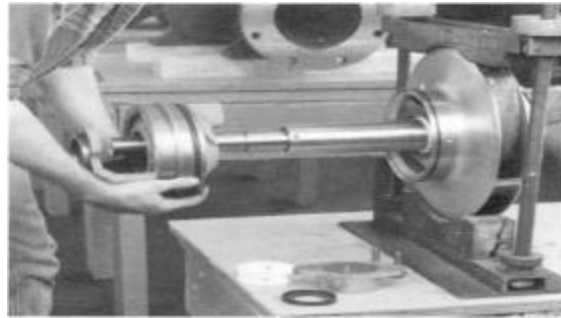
REMOCION DE LA CAJA DE EMPAQUETADURA
